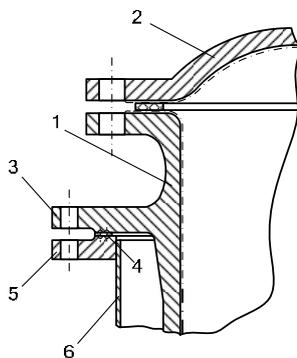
Конструкция разъемного крепления рубашки к корпусу литого аппарата:
